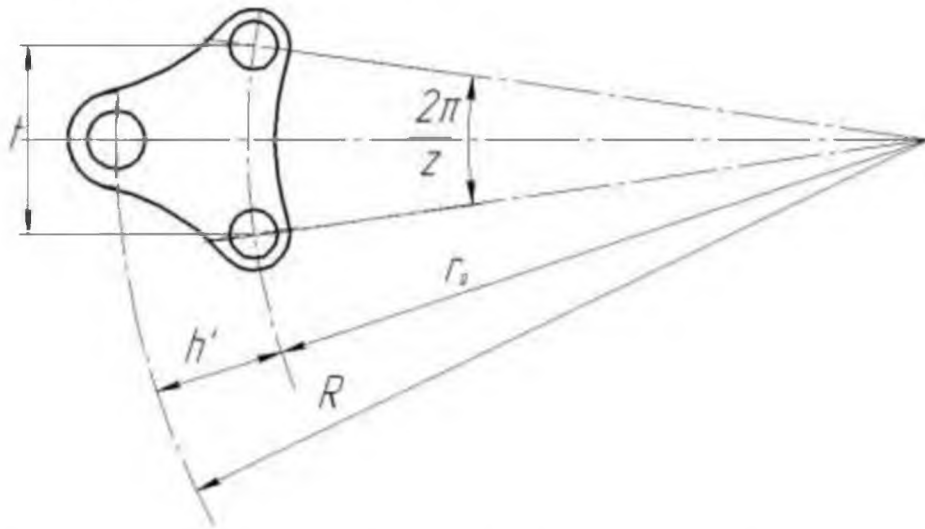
Схема ланки ланцюга для кріплення зуба-сошника
